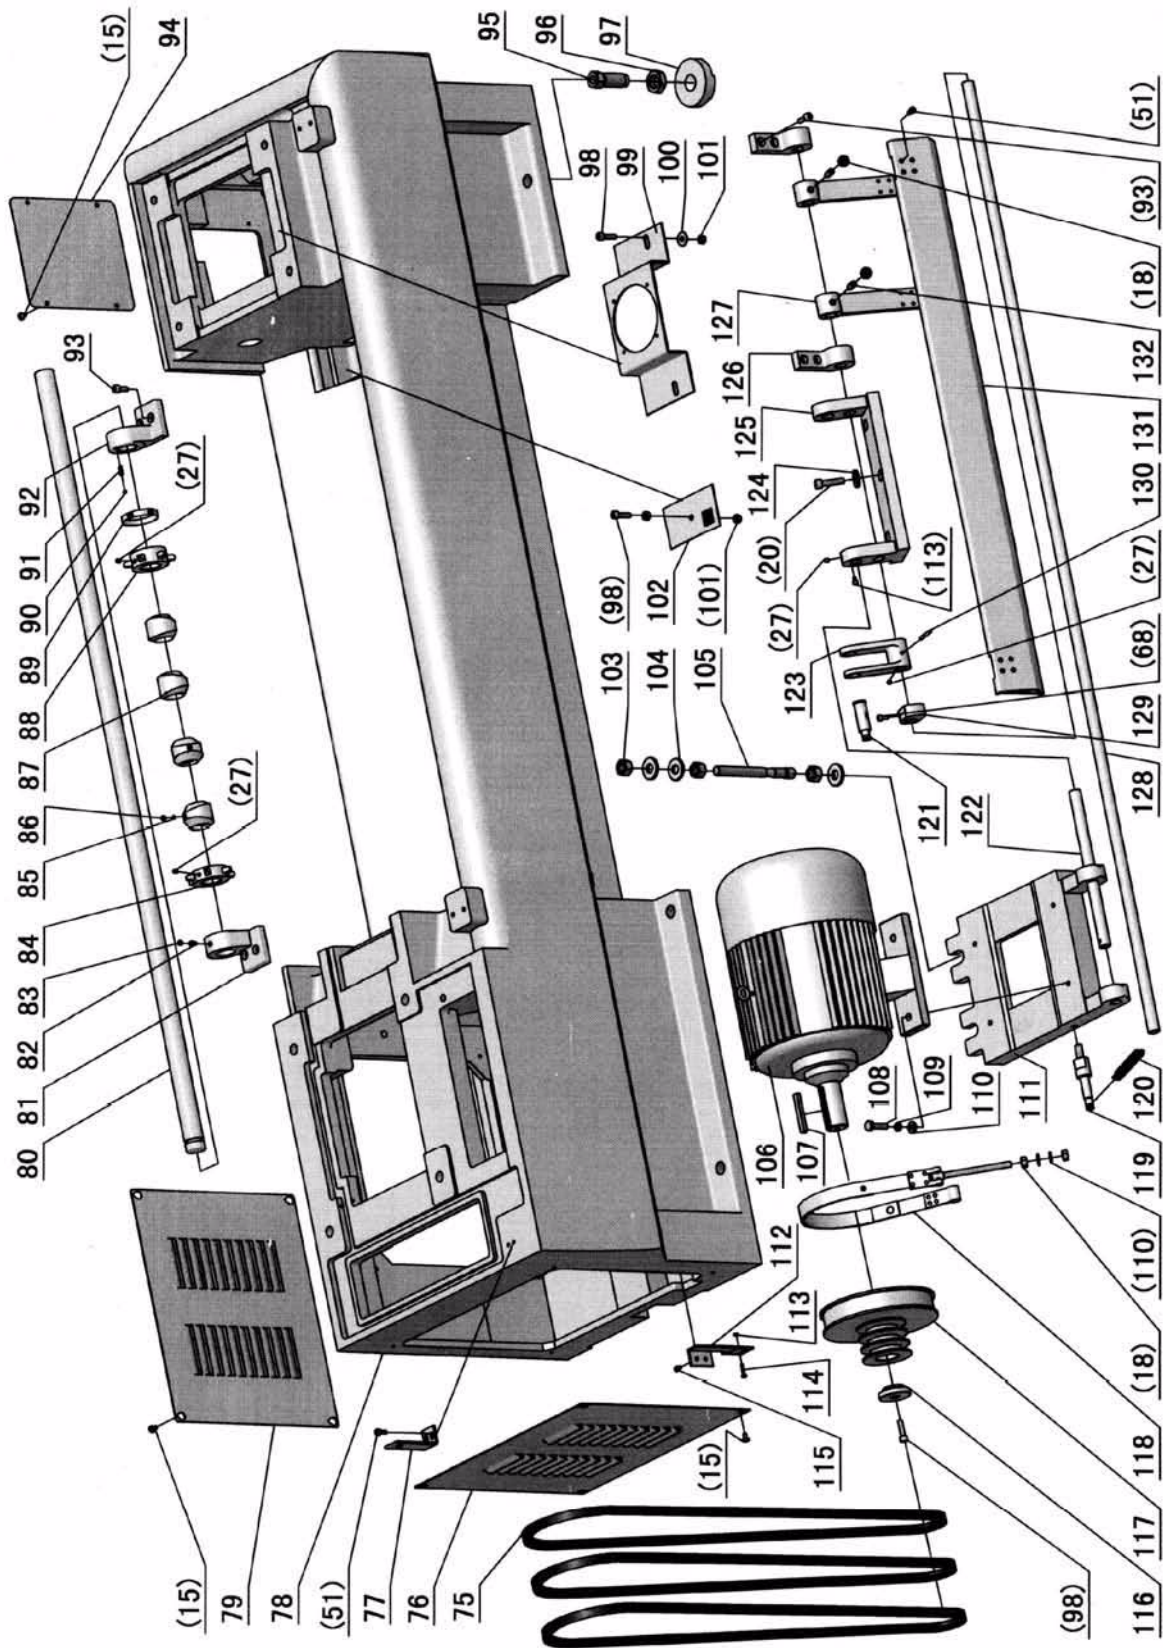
Mechanische Spindelbremse - Mechanical spindle break, actuation
